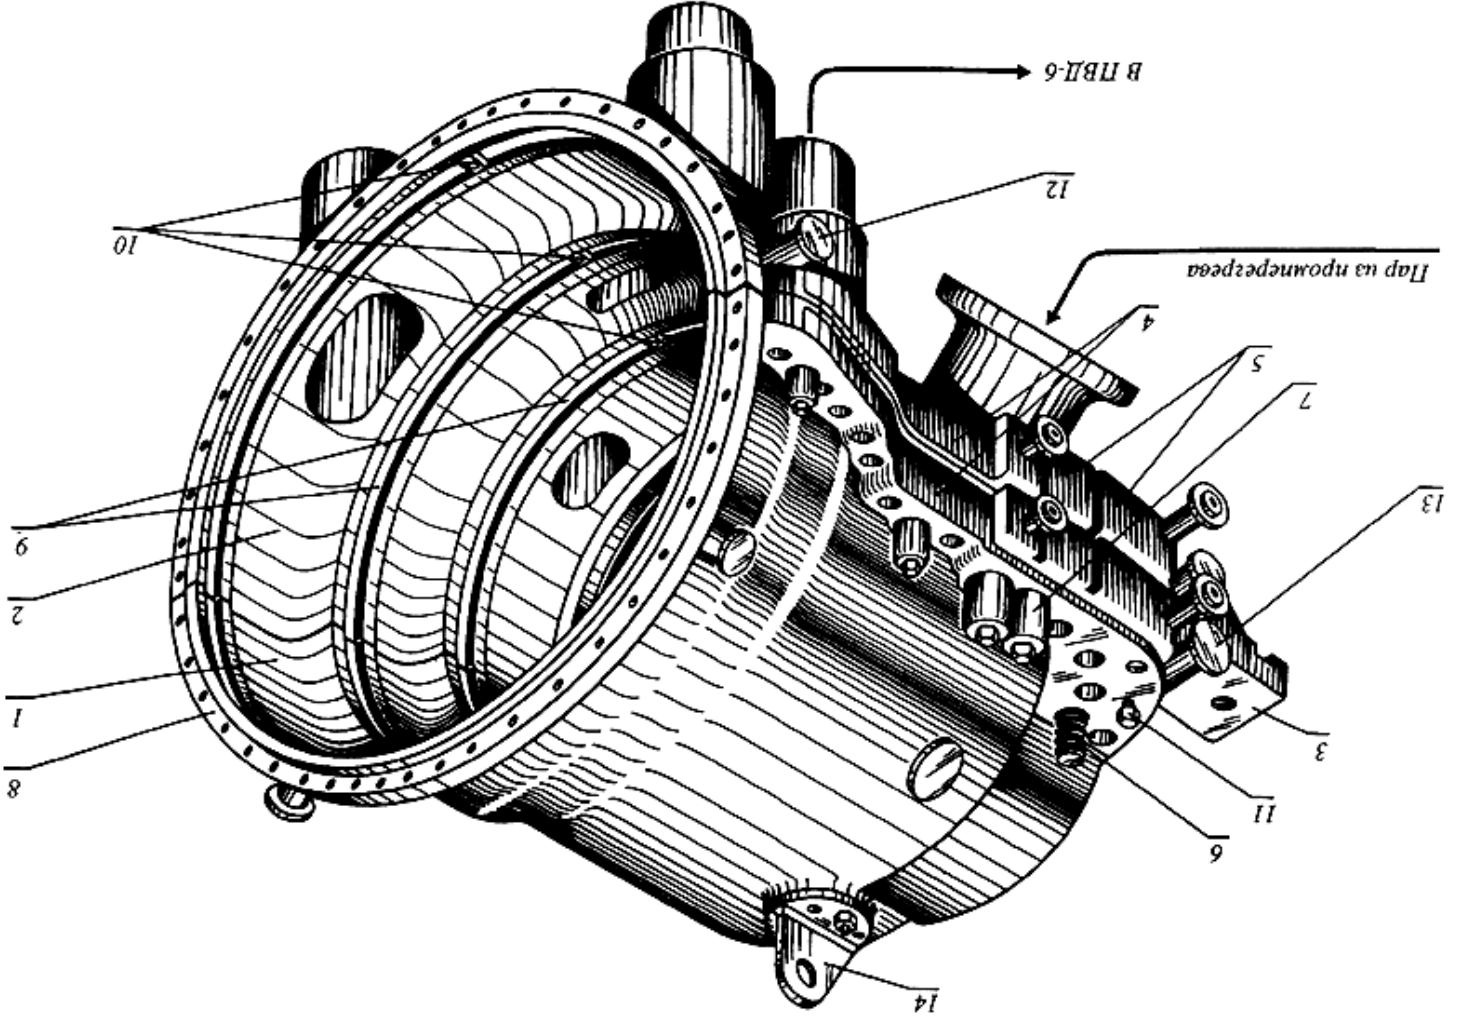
Литая передняя часть корпуса цилиндра среднего давления турбины К-300-240 ЛМ3: 1 – верхняя половина корпуса; 2 – нижняя половина корпуса; 3 – опорная лапа; 4 – фланцы горизонтального разреза; 5 – короб для обогрева фланцев; 6 – шпиль; 7 – колачковая гайка; 8 – фланец вертикального разреза со средней частью корпуса ЦСД; 9 – расточка под обоймы диафрагм; 10 – продольные шпонки; 11 – отжимной болт; 12, 13 – рым
